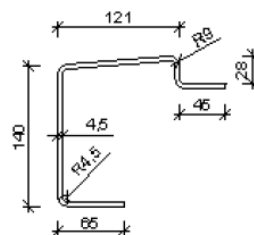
Secção transversal do perfil de porta inferior (DS) [13]
